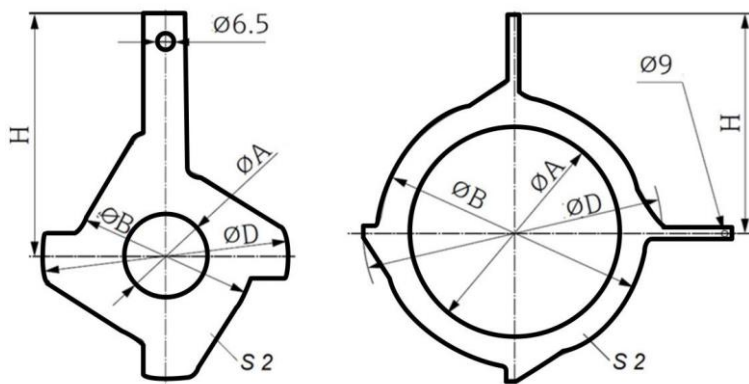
Внешний вид и габаритные размеры корпуса электронного блока для исполнения варианта 2
